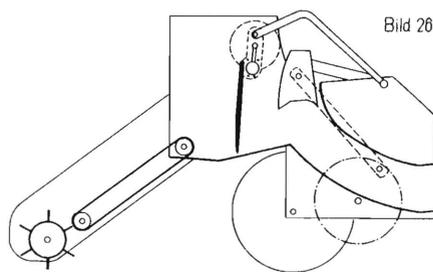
und 27. Zuführung bei Aufsammel-Schwingkolbenpressen für niedere Pressung.
